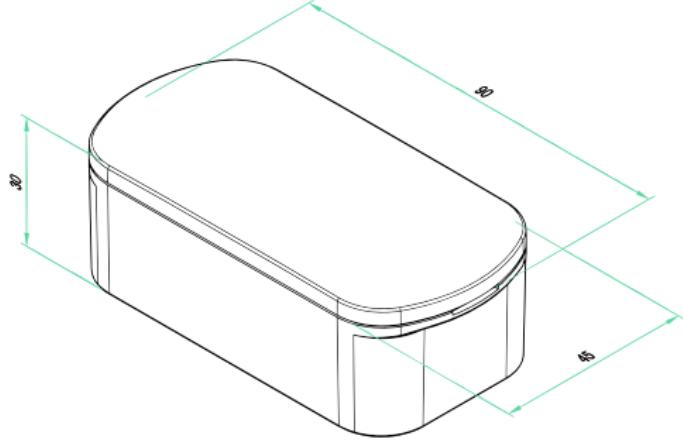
Dimensions du SIC5-9-3B TAKACHI.
